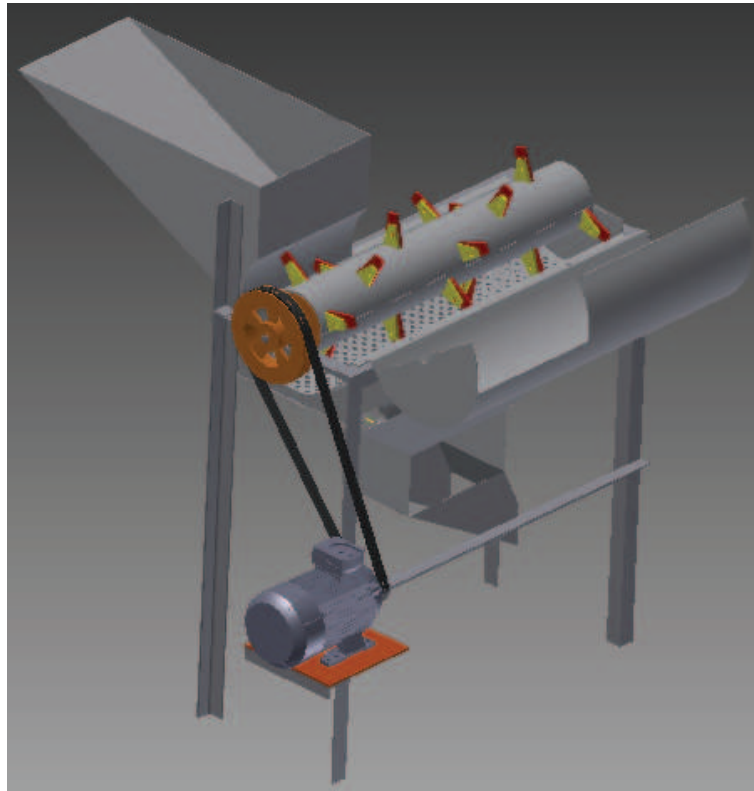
Esquema de la máquina a ser diseñada y construida
